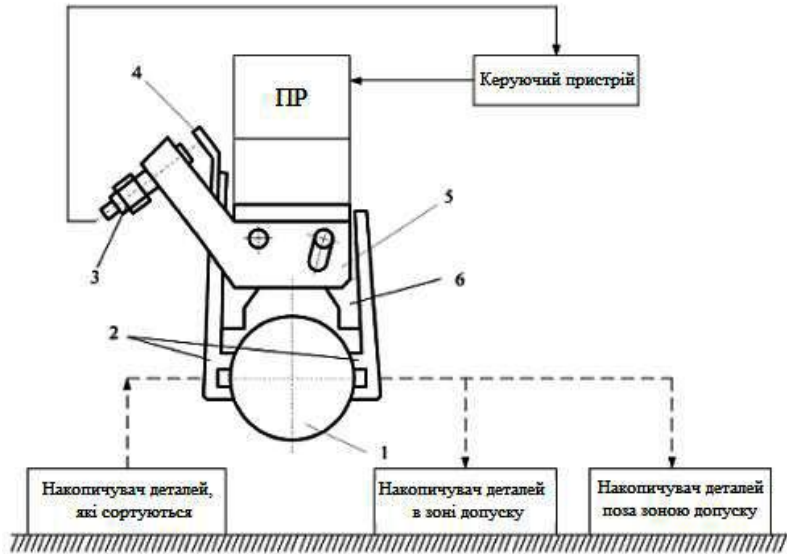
Схема суміщення операцій транспортування та контролю при сортуванні деталей: 1 – контрольована деталь, 2 – профільні губки, 3 – локаційний датчик, 4 – обмежувач, 5 – вимірювальний кронштейн, 6 – шарнірно-важільний механізм
